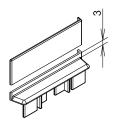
Bearbeitung der Endkappe 9C24 unten. Zuschnitt wie oben (Abb.2) und zusätzliches Entfernen des Überstandes.
